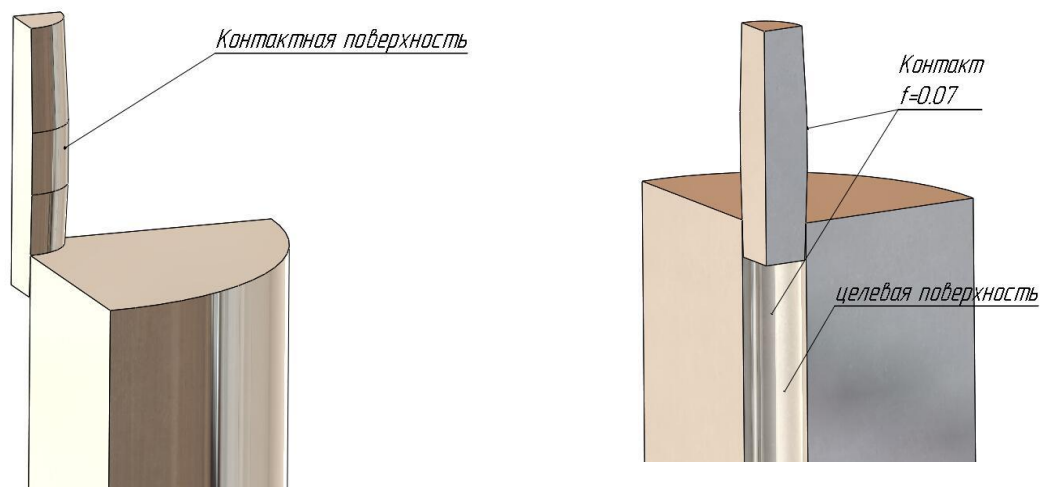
Схема -Дорн-Заготовка контактных пар
